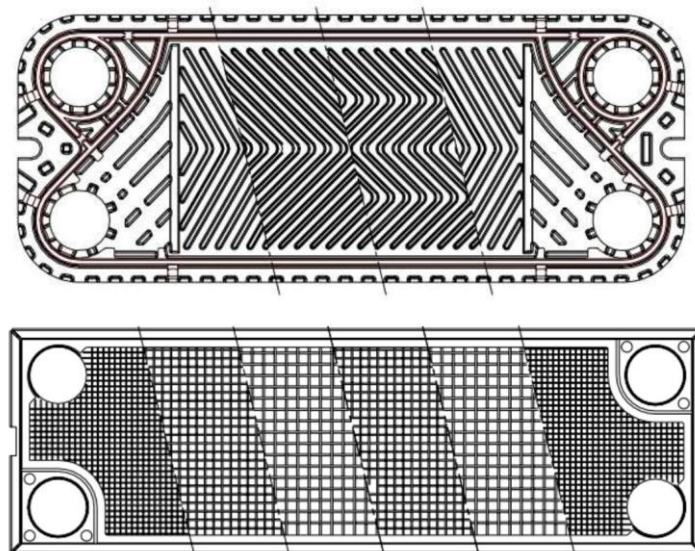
Piastra corrugata (sopra) e piastra piana (sotto)
